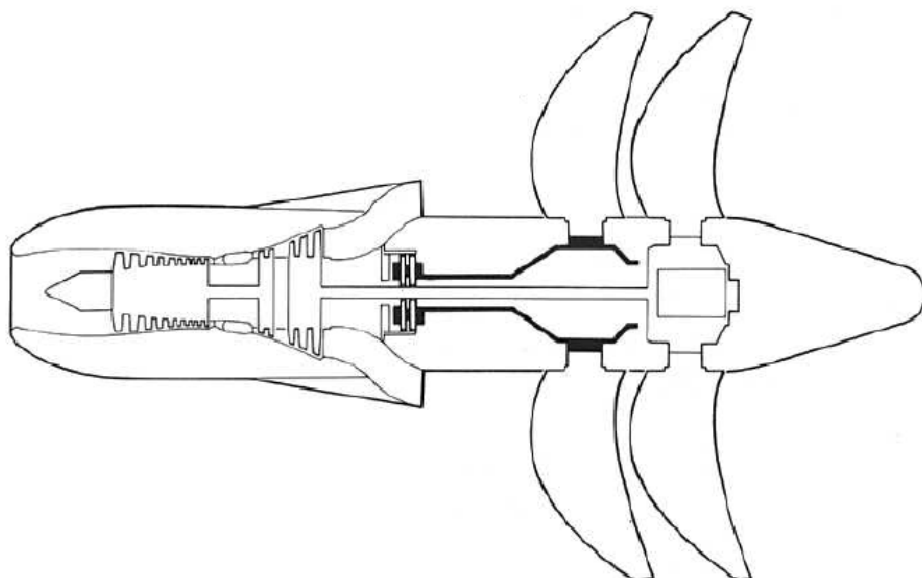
Pohonná jednotka GE-36 na testovacom lietadle [15].
